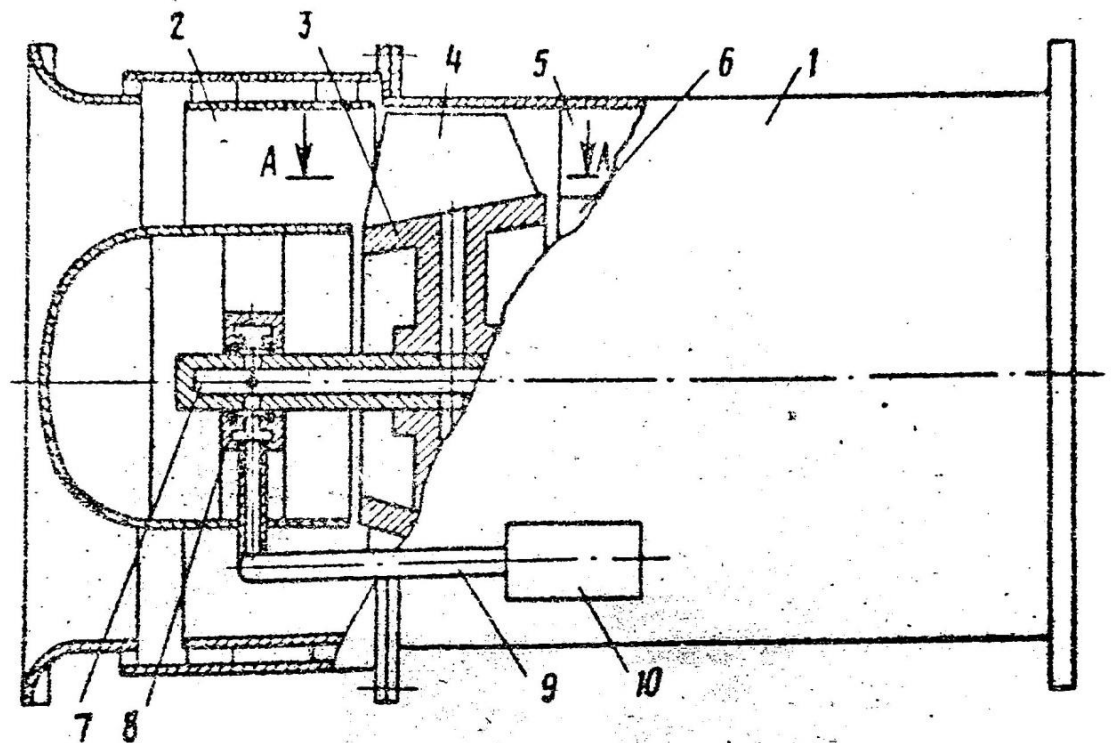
Схема конструкції вентилятора із порожнім валом. [9]
